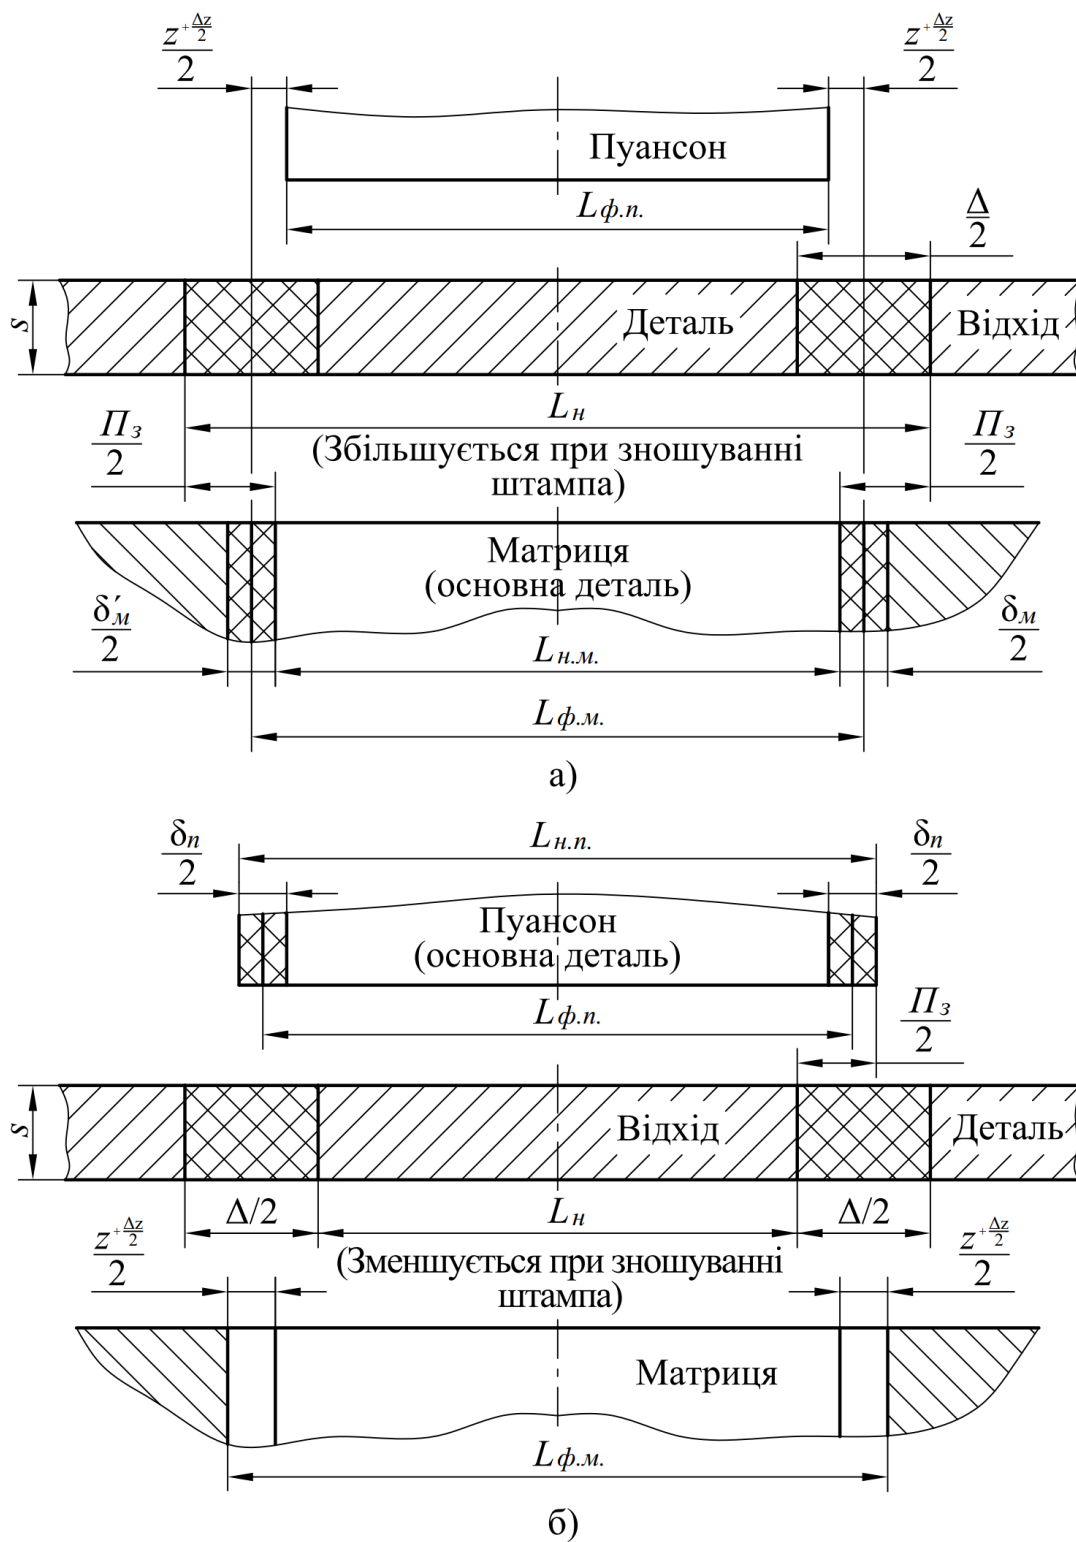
Схема розмірів і полів допусків деталі, яку штамнують, та робочих деталей штампку при їх спільному виготовленні: а – при вирубуванні; б – при пробиванні.
